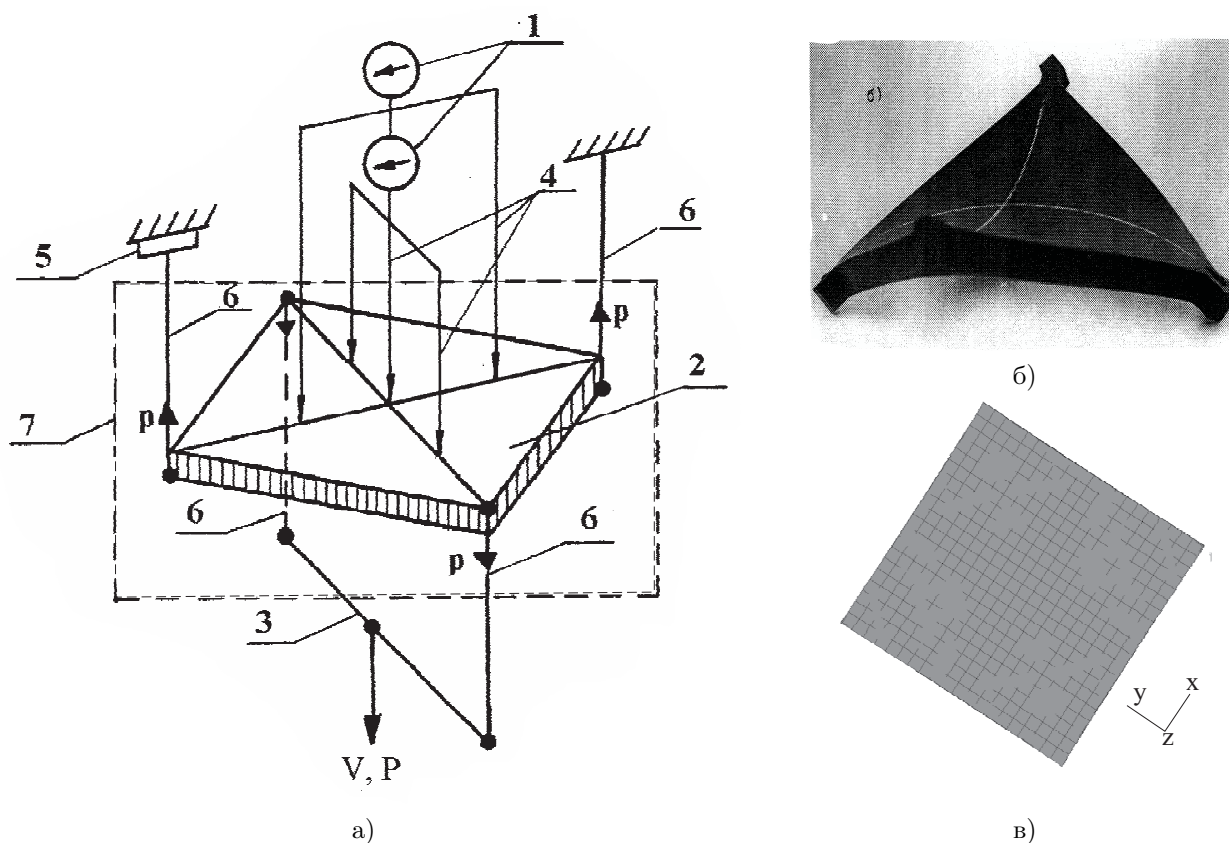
Кинематическая схема экспериментальной установки на формовку (а), вид образца детали типа “седло” (б), вычисленная заготовка (в)
